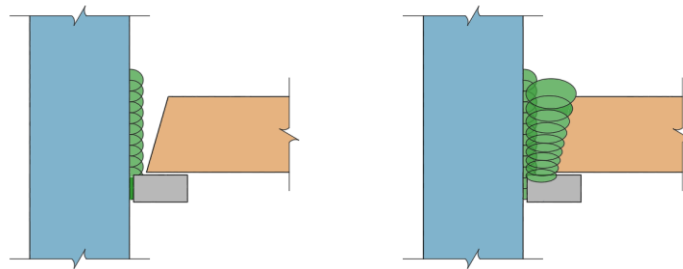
Aplicación de una primera serie de cordones de soldadura (*buttering*)
